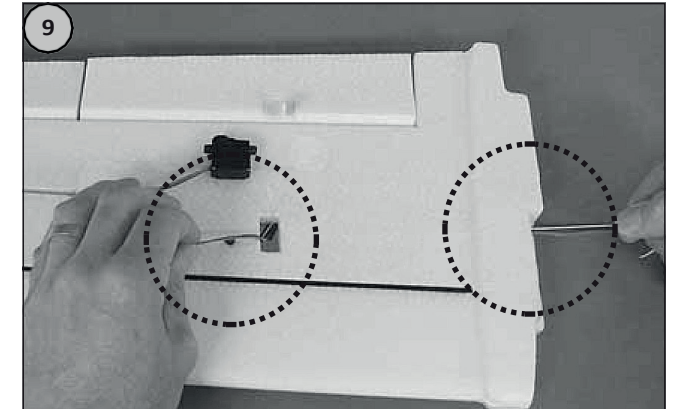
Das Servokabel durch den Kabelschacht ziehen. Anschließend die Schnur entfernen.
